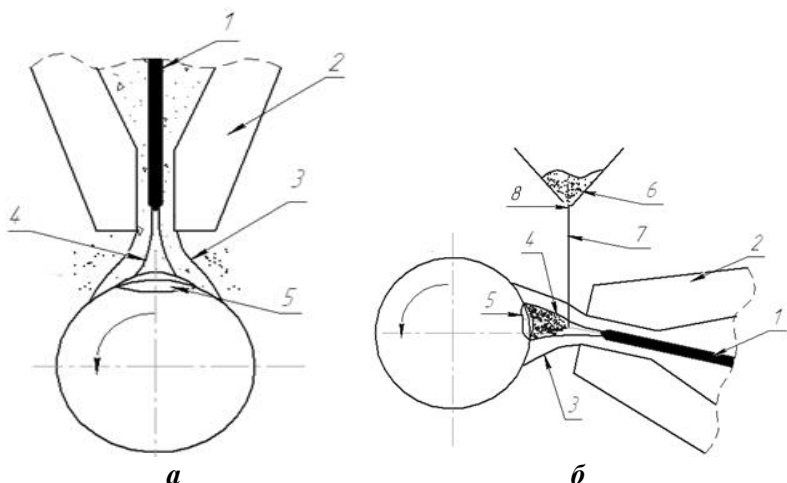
Схемы нанесения износостойких покрытий плазменно-порошковой наплавкой с подачей присадочного материала
